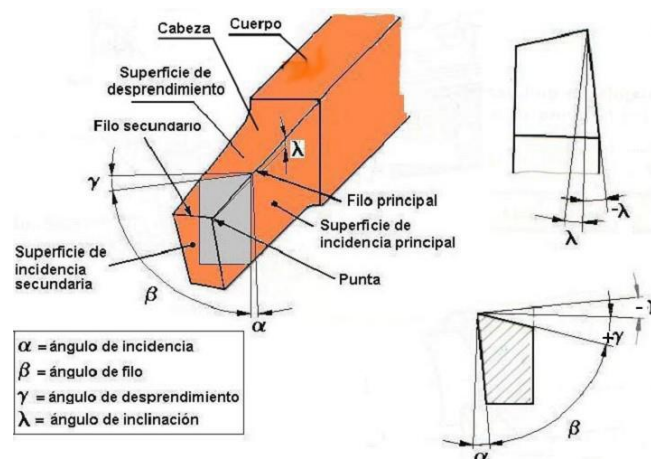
PARTES PRINCIPALES DE UNA HERRAMIENTA ELEMENTAL
